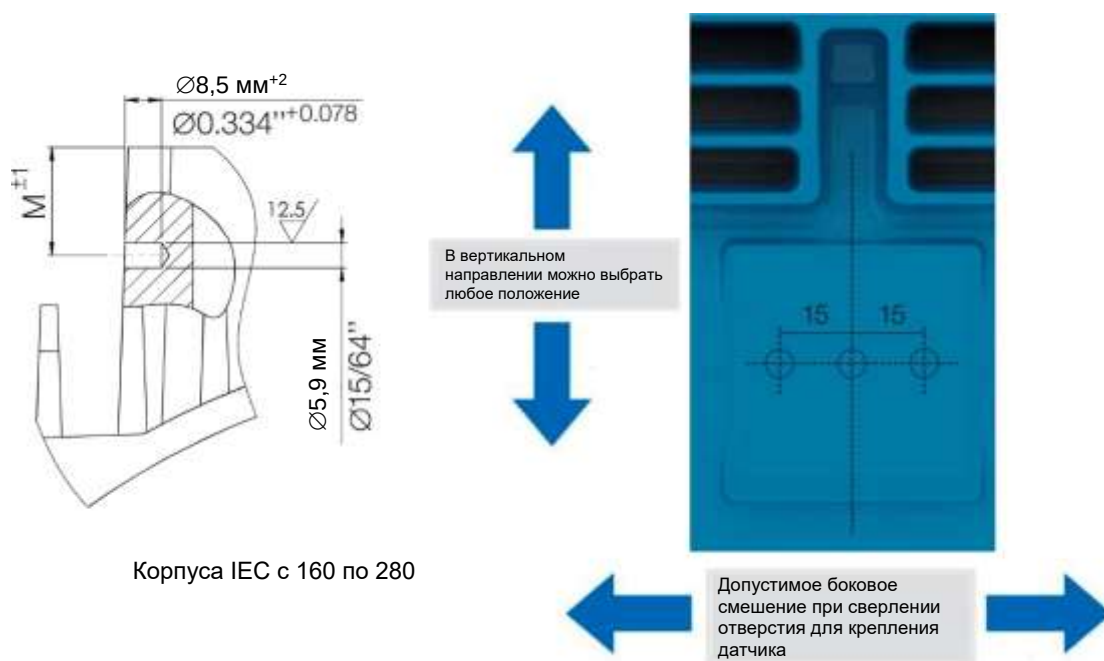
Сверление отверстия для монтажа устройства WEG Motor Scan на электродвигатель W40
